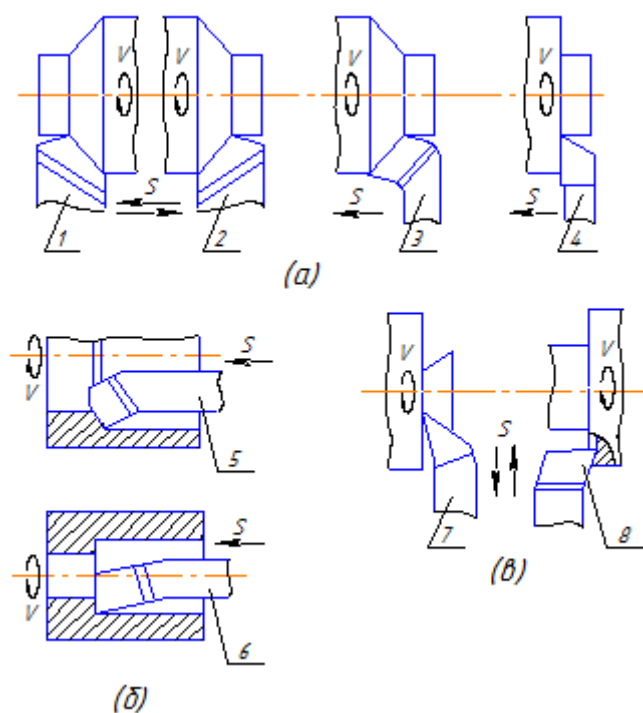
Типы токарных резцов и выполняемые операции:
